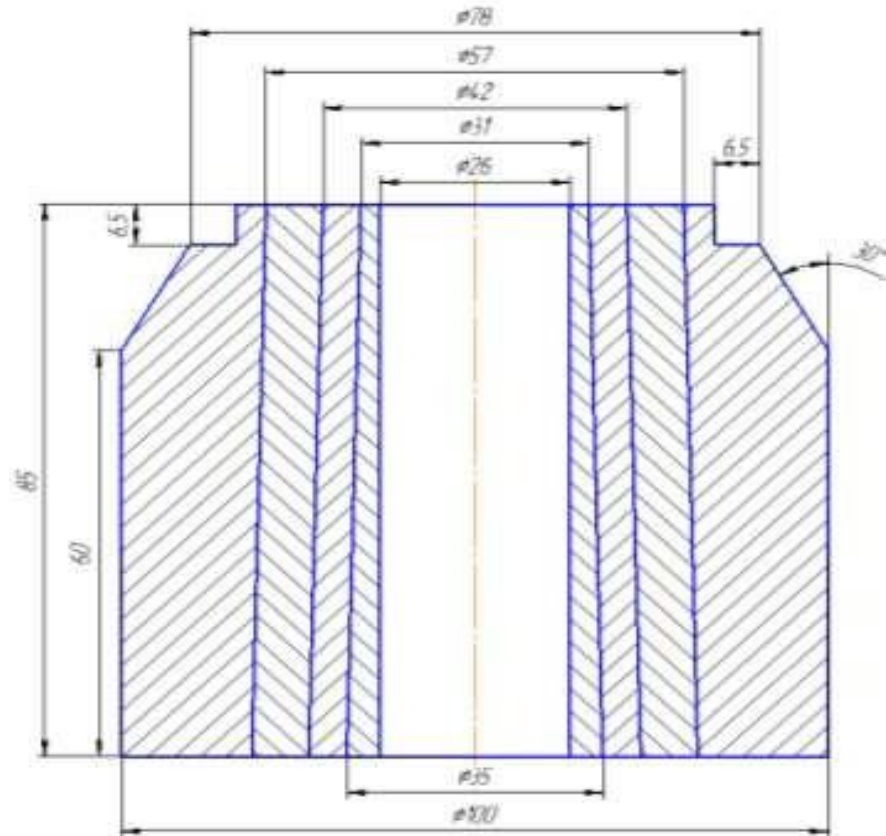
Схема бандажування матриці для зворотного видавлювання.
